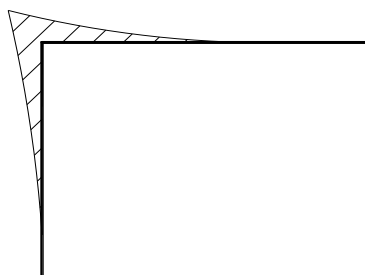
Схема формирования «недореза» на поверхности заготовки детали
